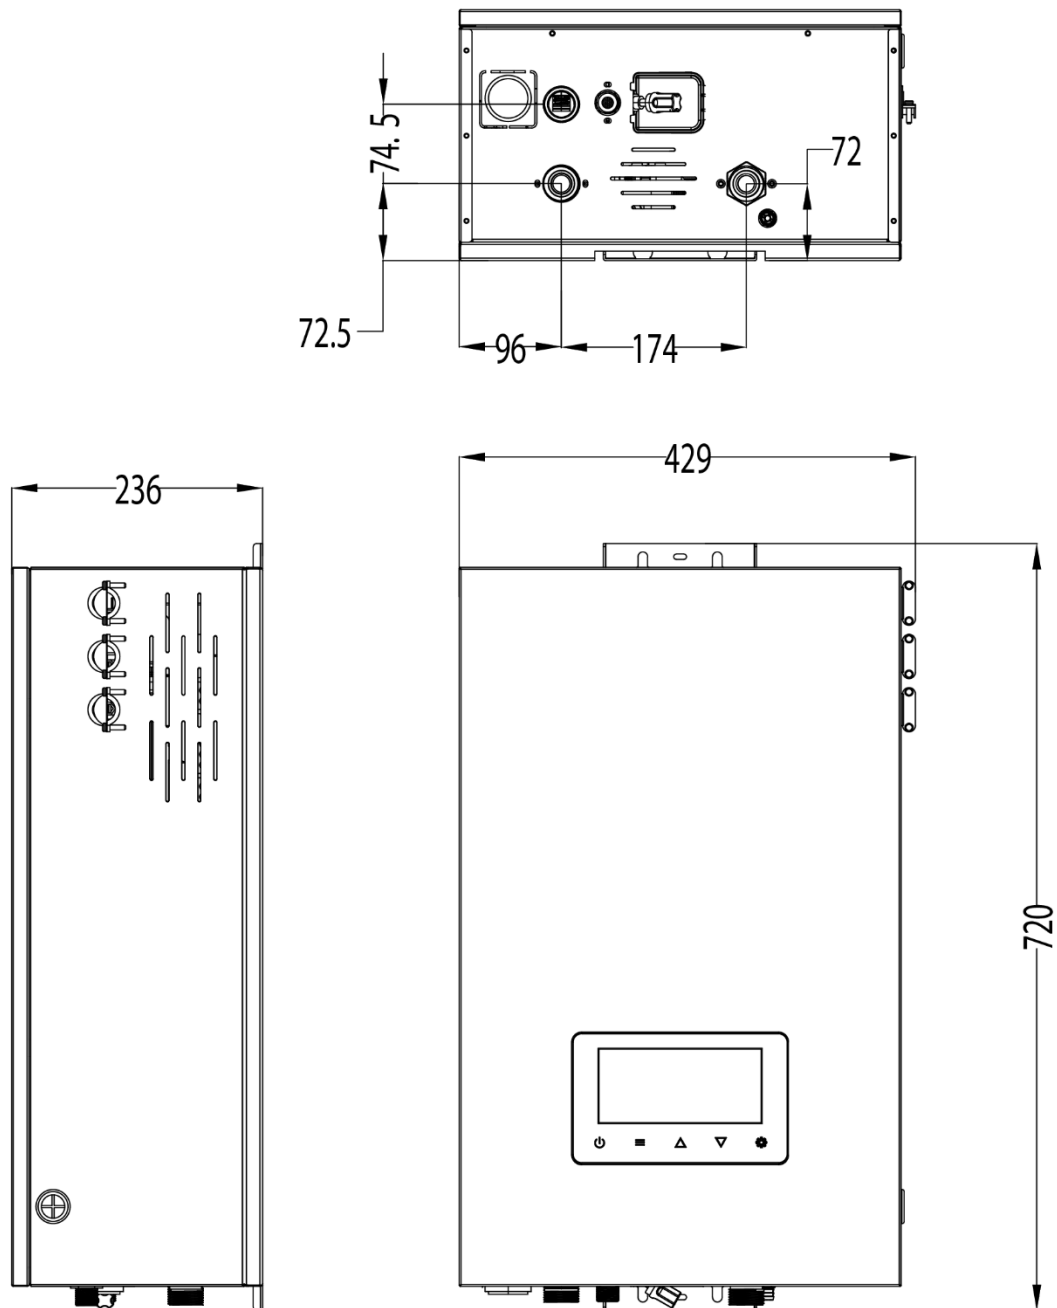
(Dimensions chaudière et emplacement des ports de connexion)
